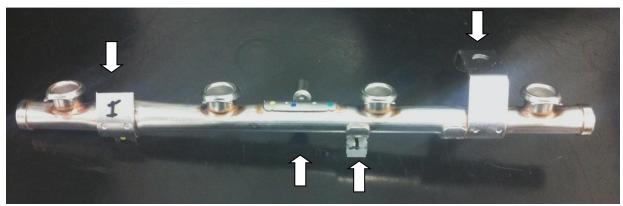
Flauta de alimentação de sistema de injeção, brasada a 1100°C. As setas indicam as hastes de fixação de aço inoxidável ferrítico AISI 430, que fraturaram durante operação de calibração e desempeno.
